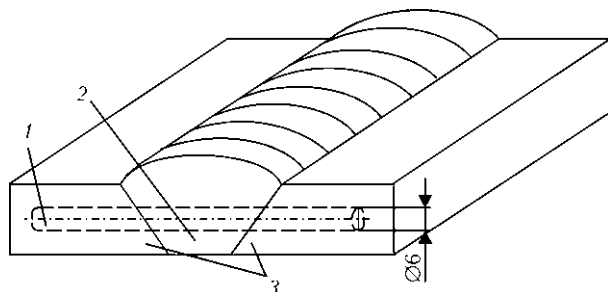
Схема вырезки образцов-имитаторов для испытания на установке Gleeble: 1 — место вырезки образца; 2 — сварной шов; 3 — свариваемые пластины
